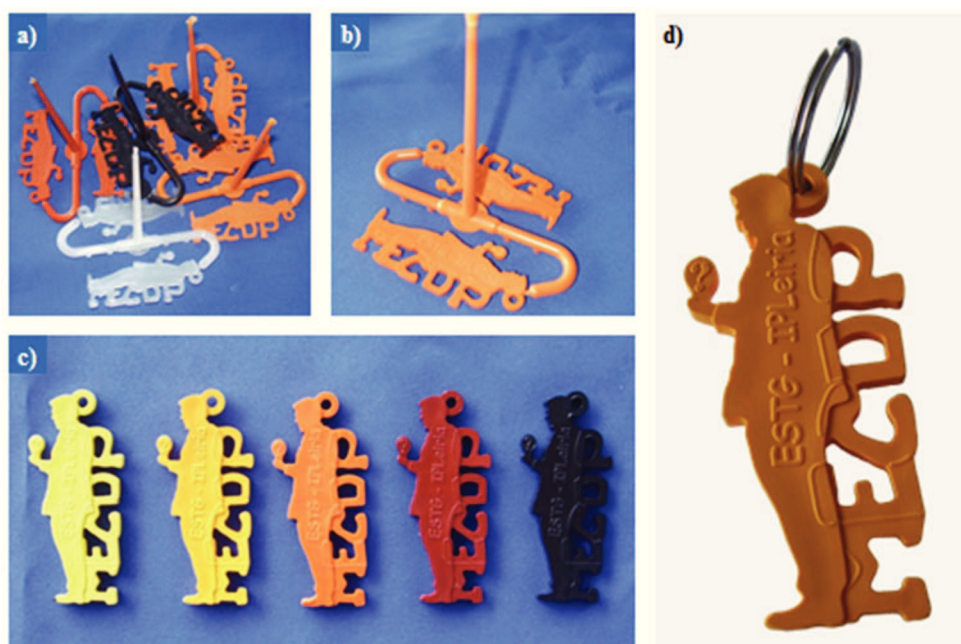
Peças processadas por injeção com zonas moldantes em aço: a) e b) Moldações; c) e d) porta-chaves (separados do gito e dos canais).
